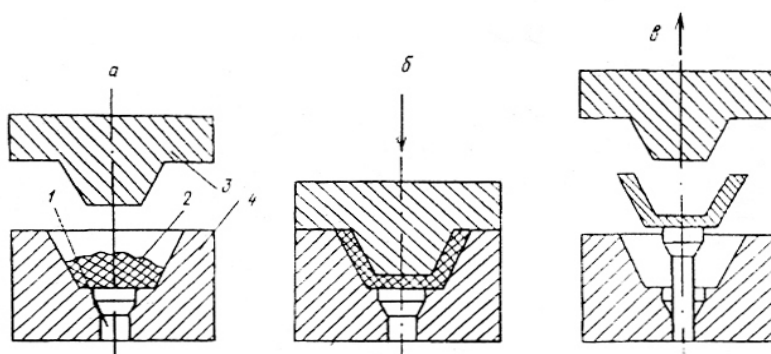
Схема изготовления изделий методом компрессионного формования
